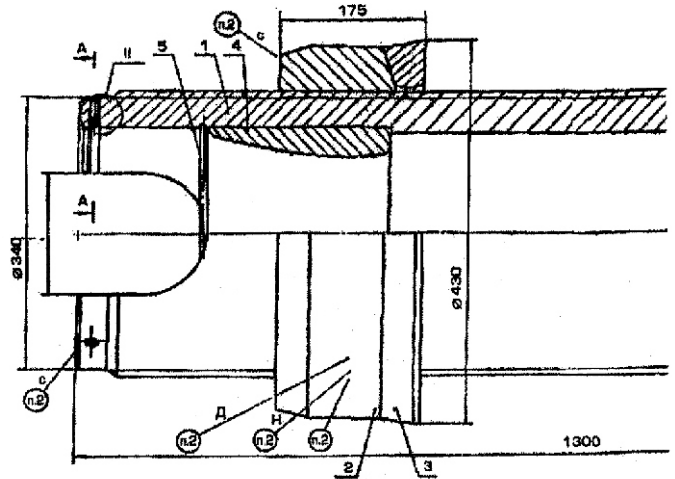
Схема з'єднання гайки і гільзи анкерного пристрою АК:
